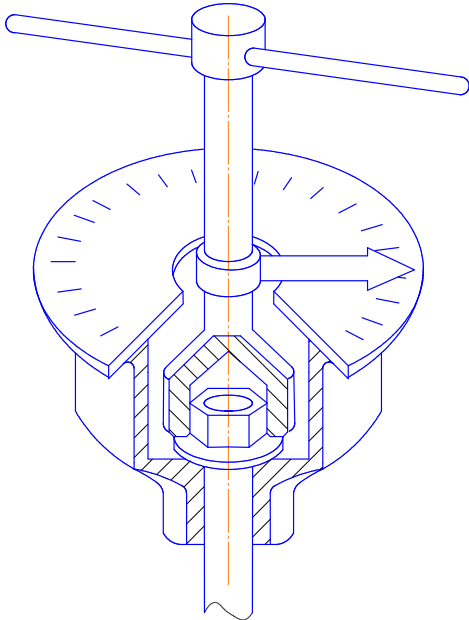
Ключ для затягування з'єднань, які контролюються за кутом повороту гайки
